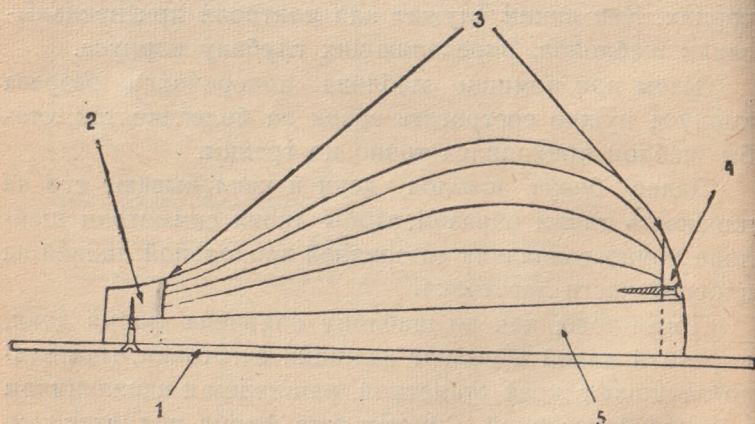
Форма корпуса с закрепленными стойками и одной клепкой:
